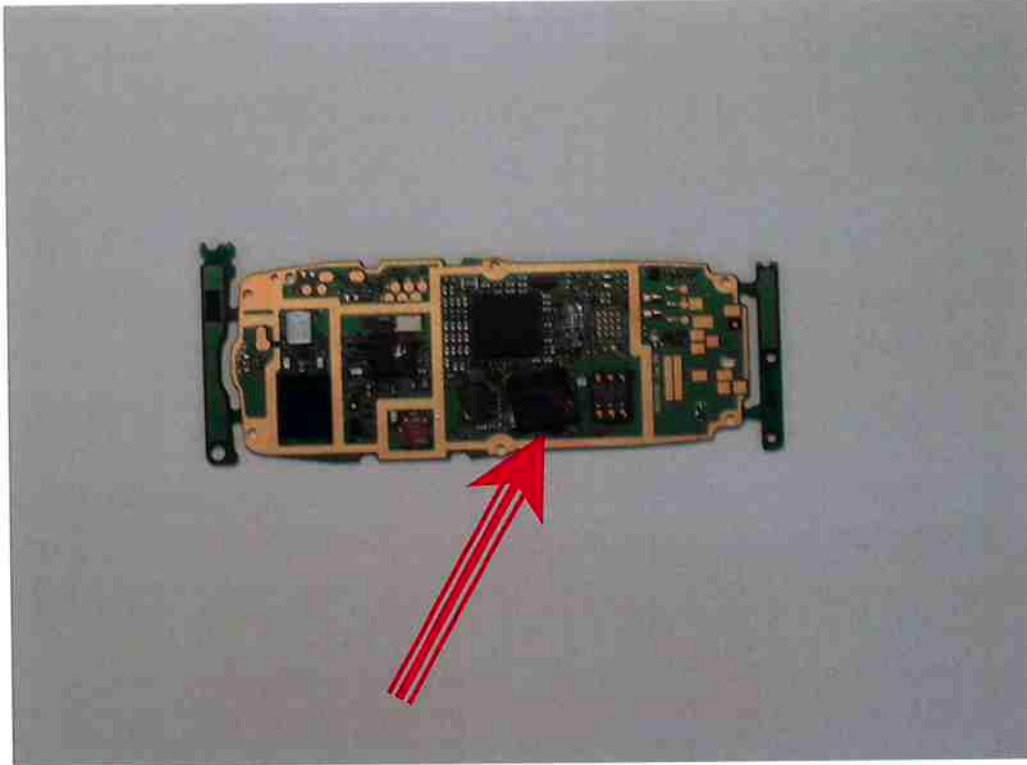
Componente do Tipo BGA Incorretamente Posicionado
